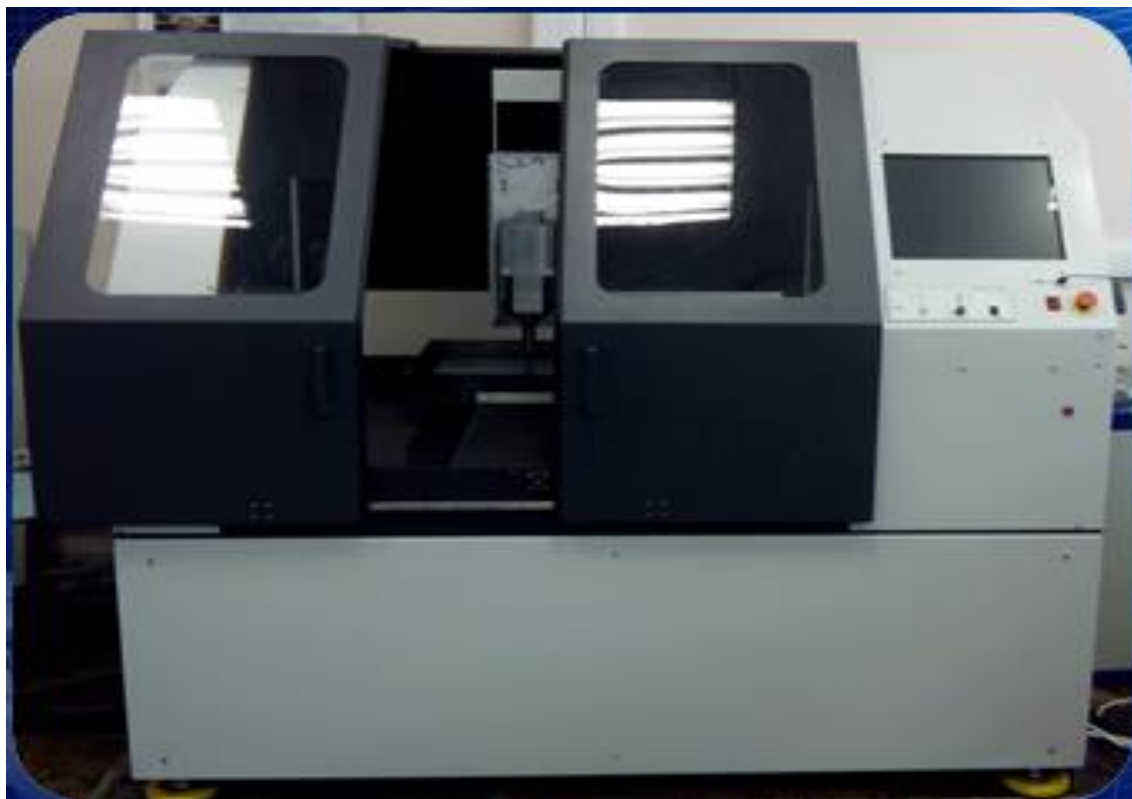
Пятикоординатный ультразвуковой станок (МУЗС-1)
